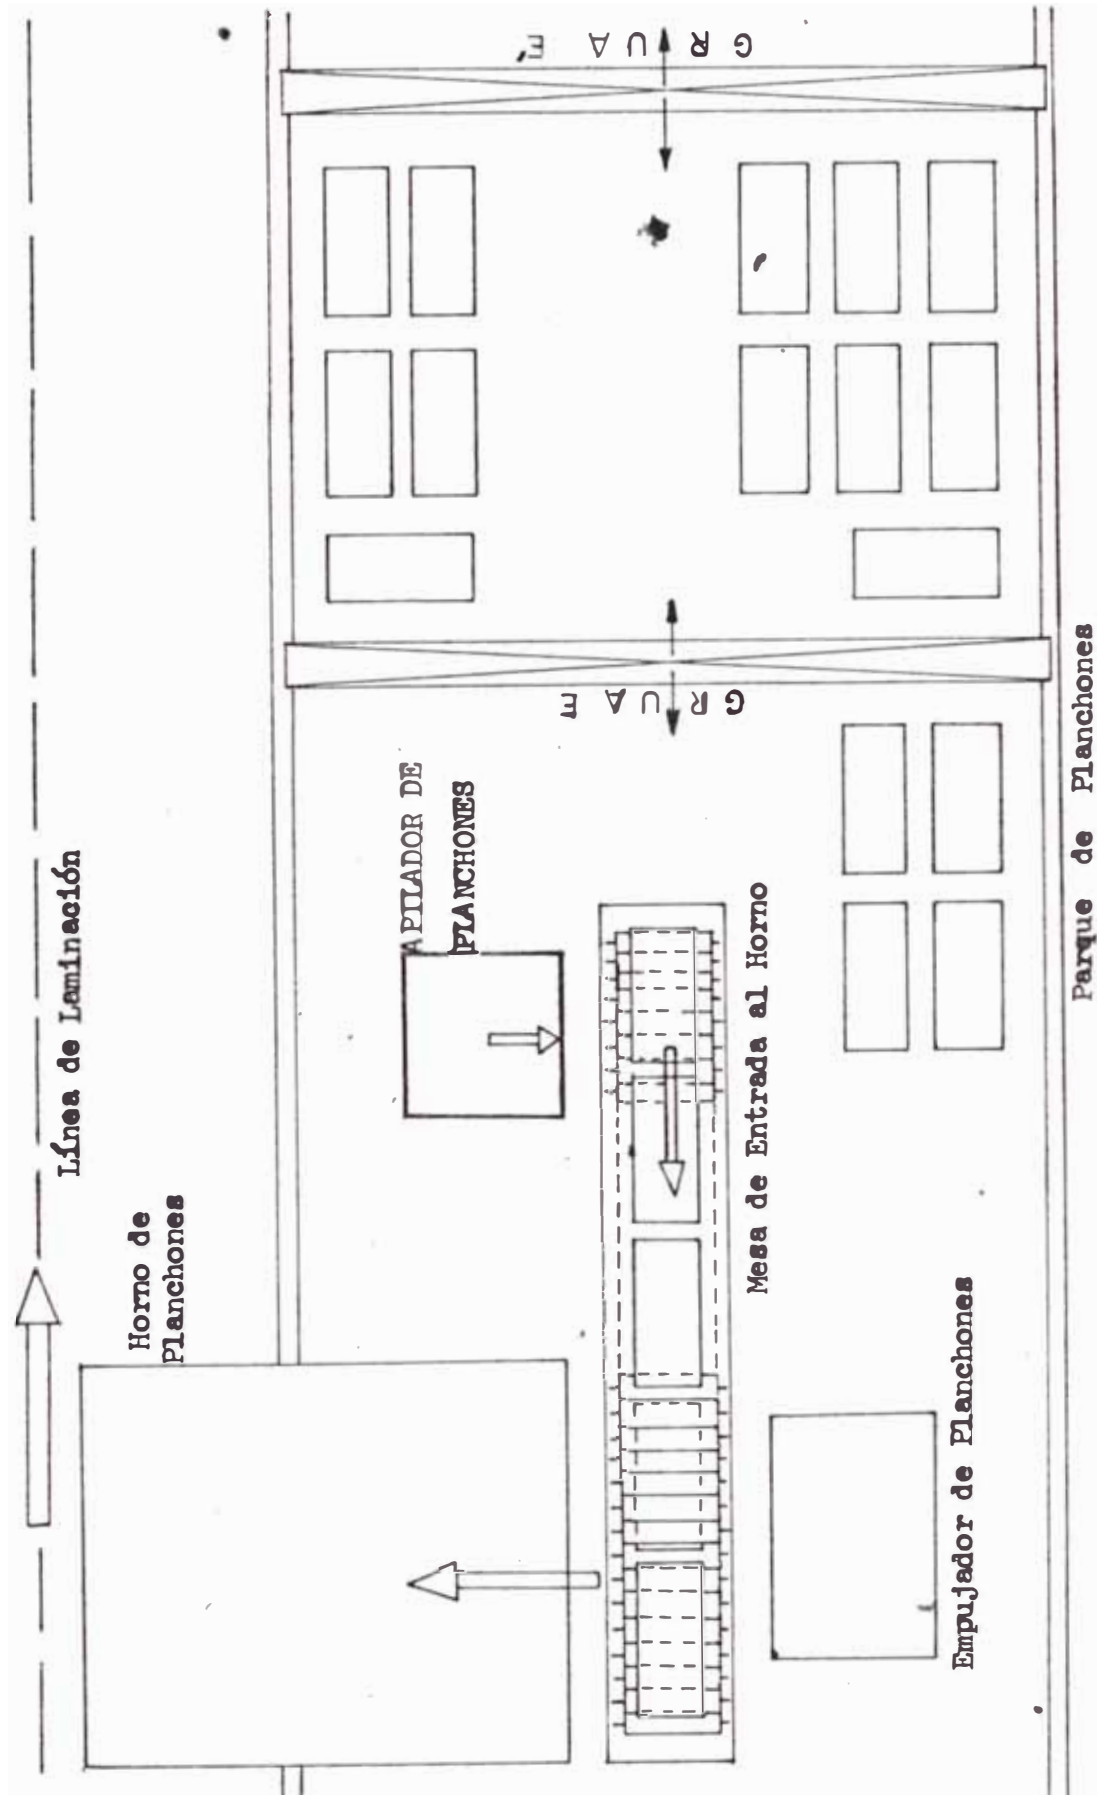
UBICACIÓN DEL APIADOR DE PLANCHONES
